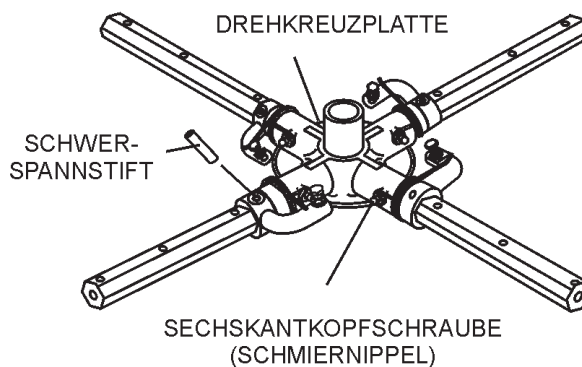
Entfernen des Schwerspannstifts und Schmiernippels
